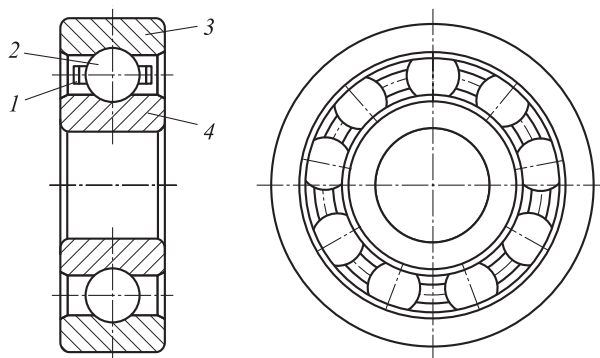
Конструктивная схема радиального шарикового подшипника:
